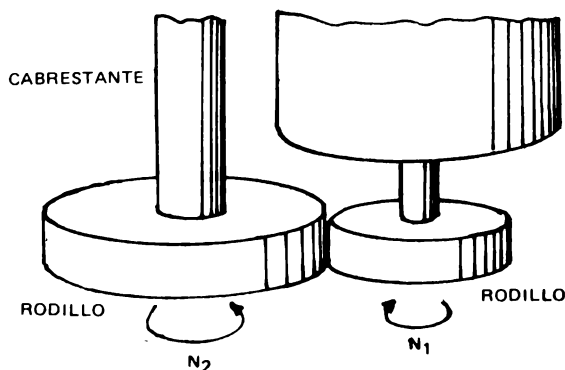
Disposición esquemática de la transmisión del movimiento mediante rodillos de fricción rozantes entre sí.
